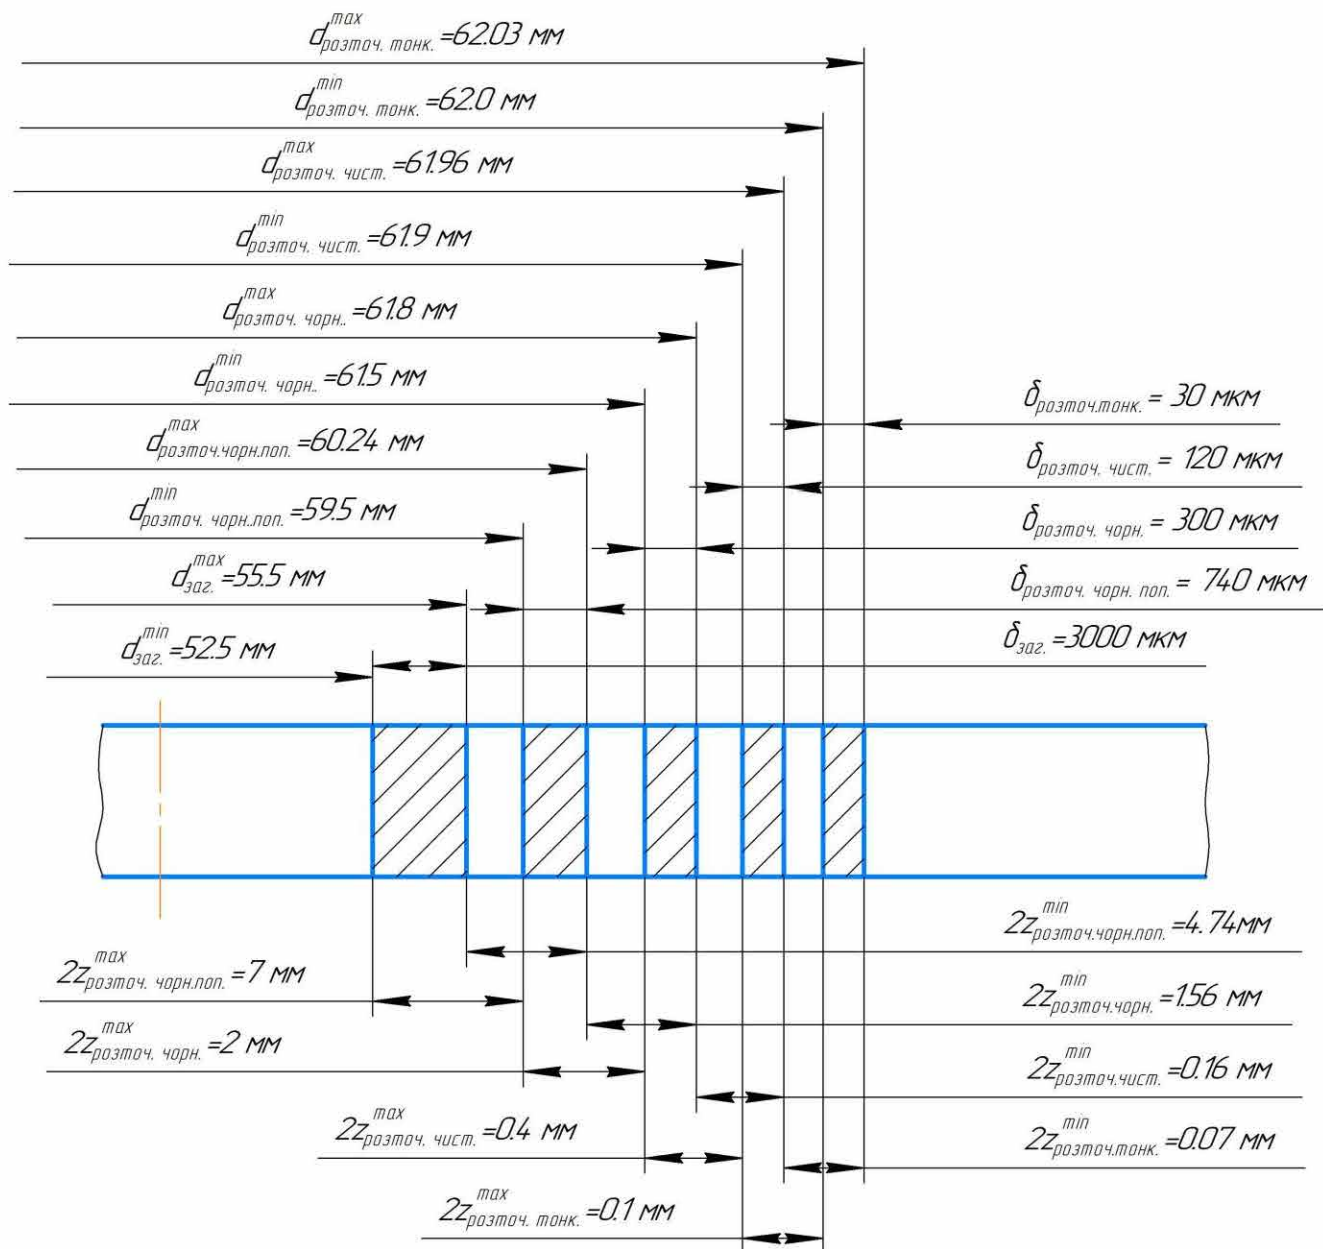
Схема графічного розташування припусків і допусків для поверхні  $\text{Ø}62^{+0.03}$
